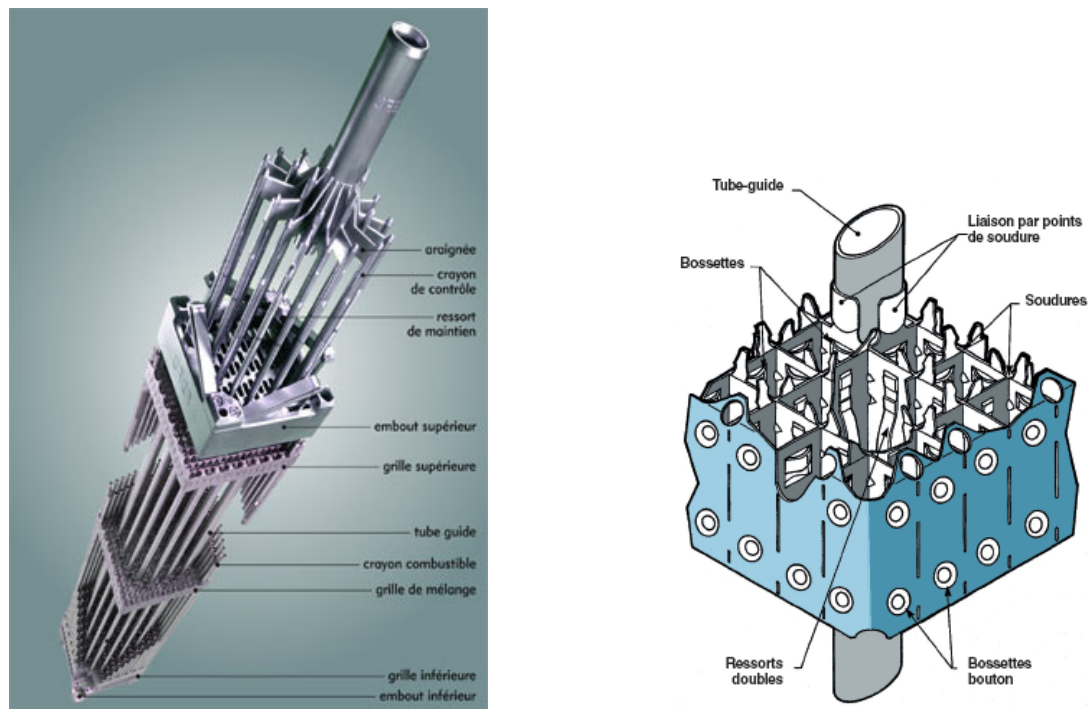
a) Assemblage combustible. b) Schéma d'une grille d'assemblage [19]
